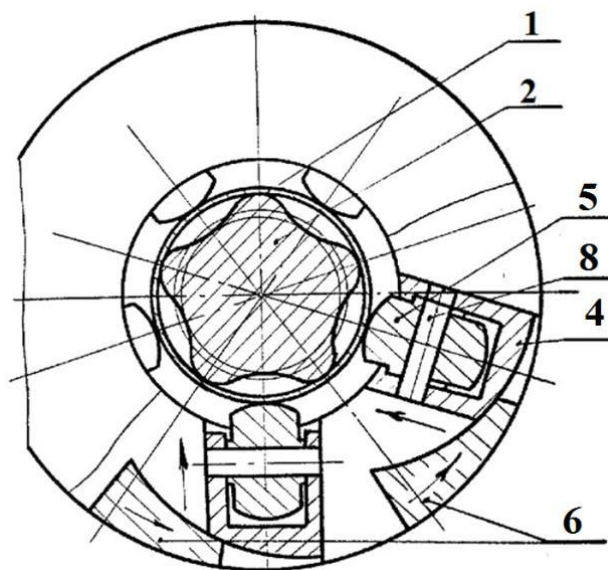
Схема початку формування гвинтоподібної деталі обкатною ГОЛОВКОЮ
